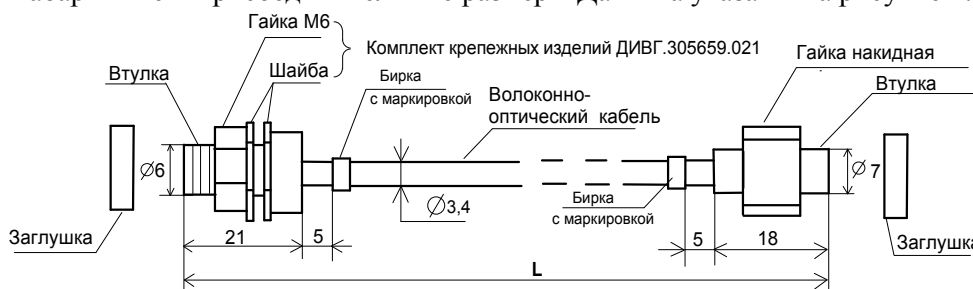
Габаритные и присоединительные размеры Датчика
